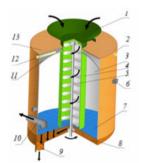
СВЧ-установка с коаксиальным спиральным резонатором: 1 — неферромагнитная загрузочная емкость; 2 — неферромагнитный наружный цилиндр; 3 — неферромагнитный коаксиальный резонатор; 4 — неферромагнитный внутренний спиральный цилиндр; 5 — электроприводной фторопластовый шнек; 6 — магнетроны с волноводами и вентиляторами; 7 — нижнее перфорированное основание; 8 — неферромагнитная накопительная емкость; 9 — запредельный волновод с шаровым краном; 10 — диэлектрическая труба пневмотранспортера; 11 — керамическая кольцевая сферическая поверхность; 12 — электрогазоразрядные лампы; 13 — неферромагнитные коронирующие щетки
